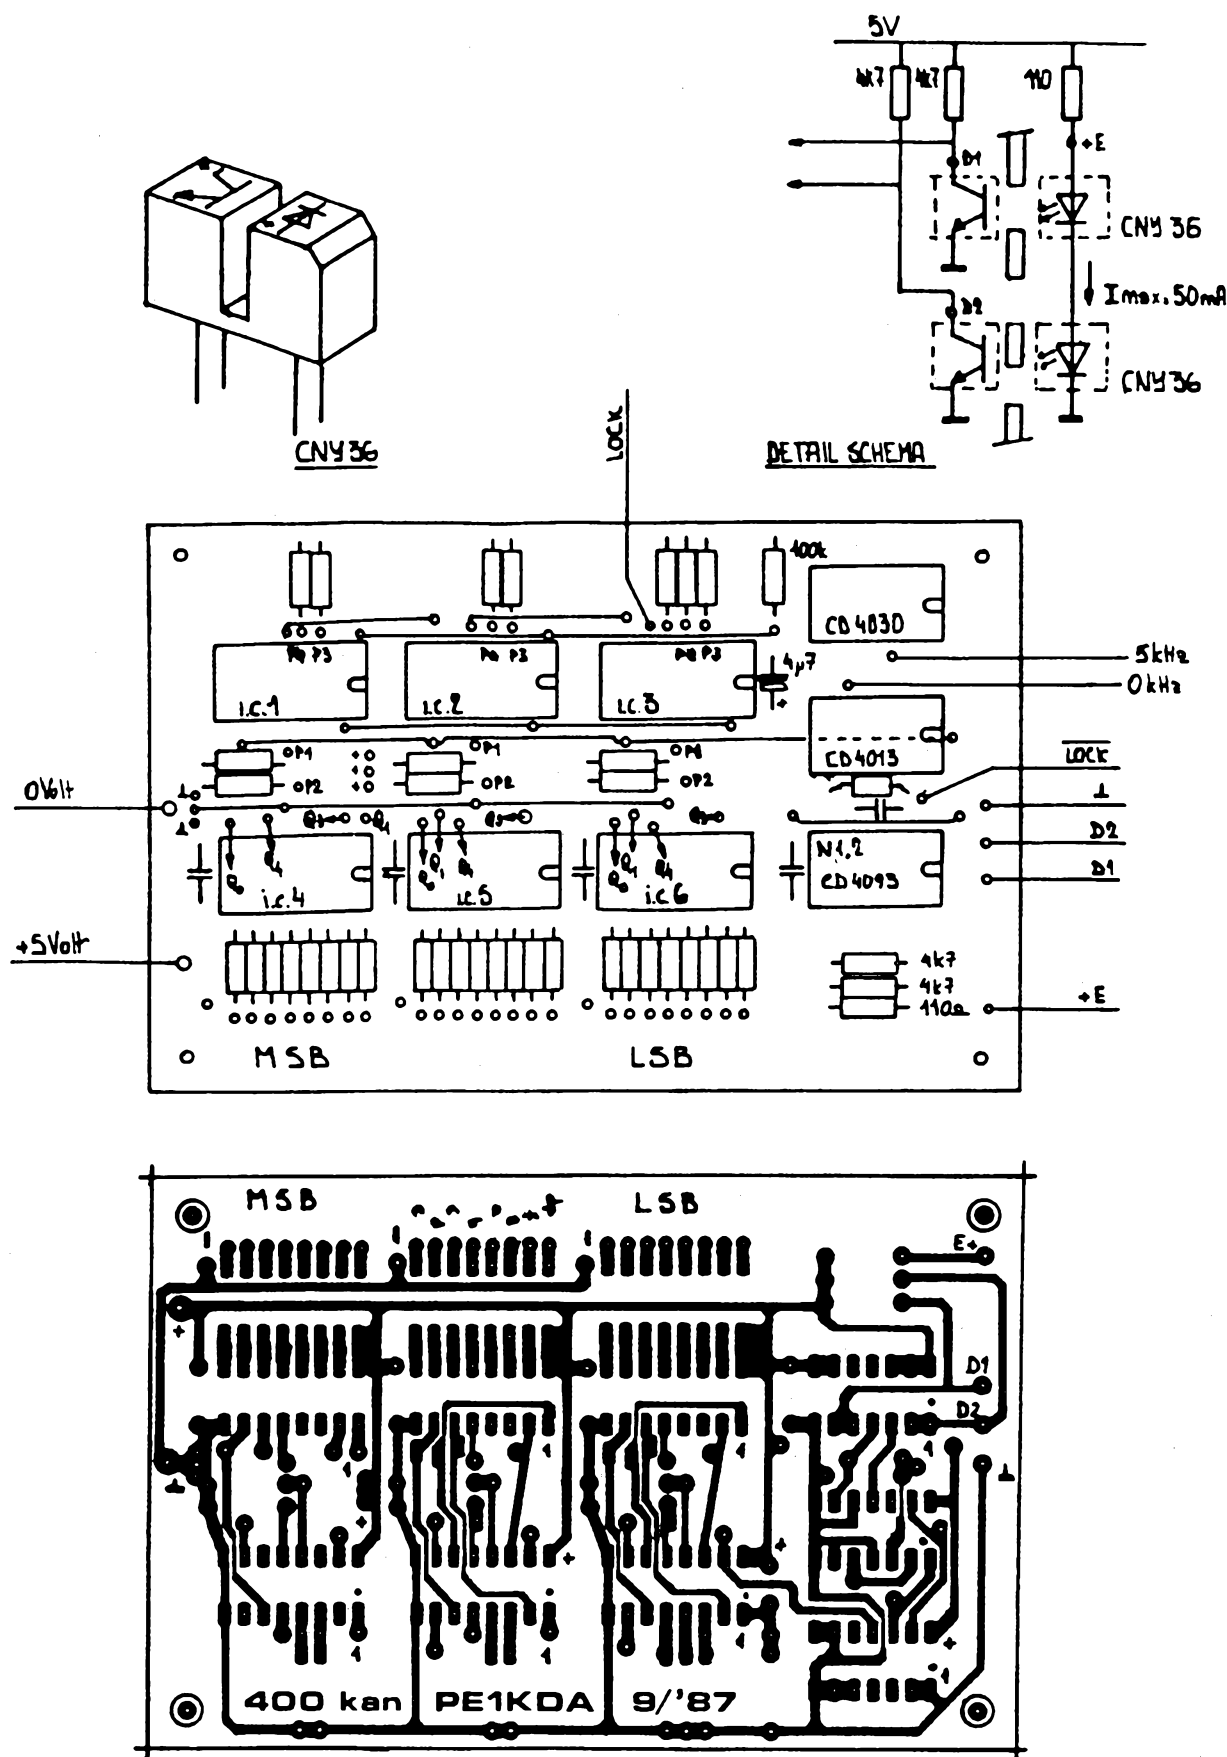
Constructie van de CNY36. Componentenopstelling en lay-out van de print.
